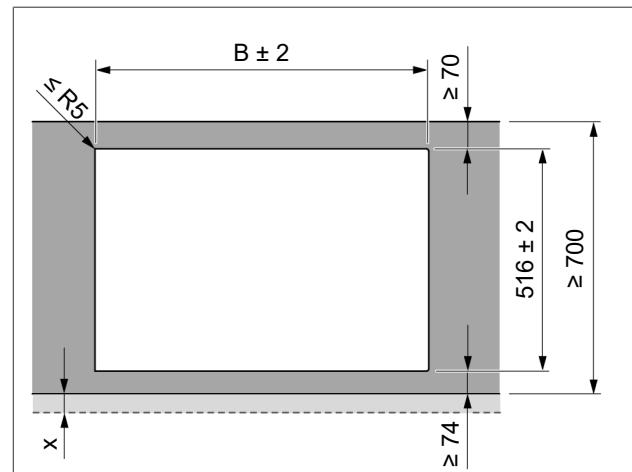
Rozmery drážky pre zapustenú montáž
